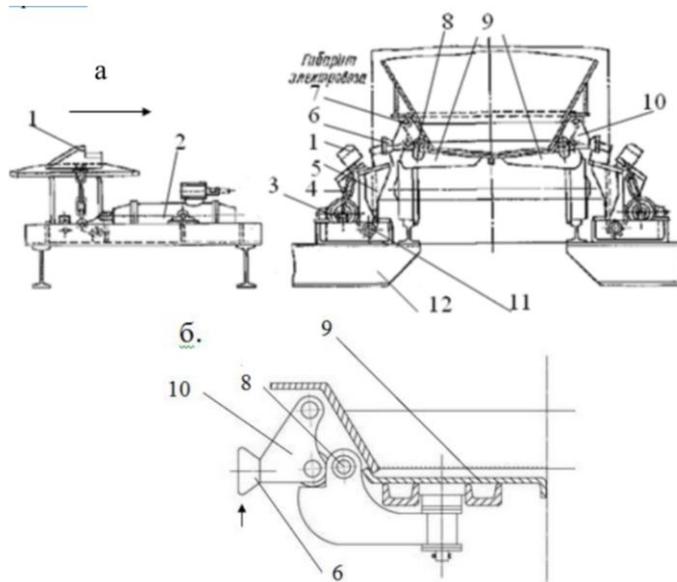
Устройство для открывания днищ: а – общий вид, б – положение роликового замкового устройства при закрытом
